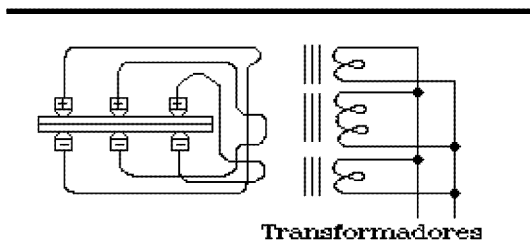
Soldagem com Conexão Elétrica em Paralelo.
